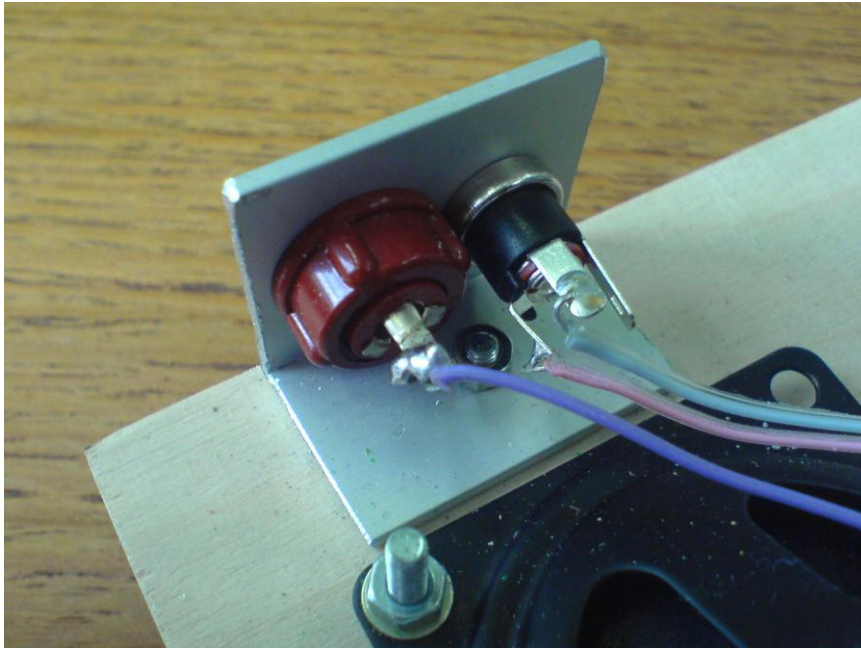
Montagewinkel mit Stromversorgungsbuchse und Antennenstecker
